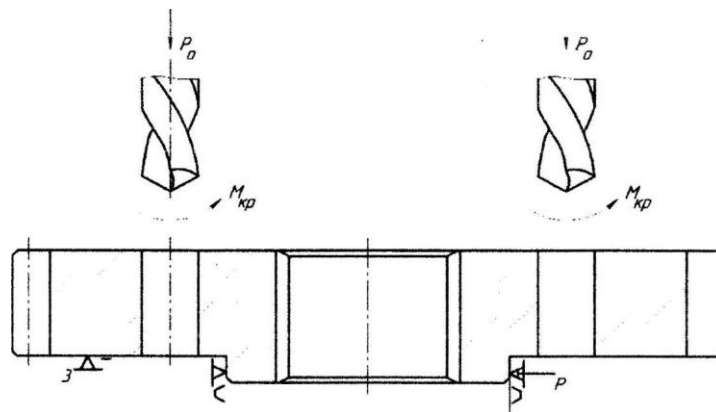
Схема базування заготовки в пристосуванні та сили, що діють на заготовку
